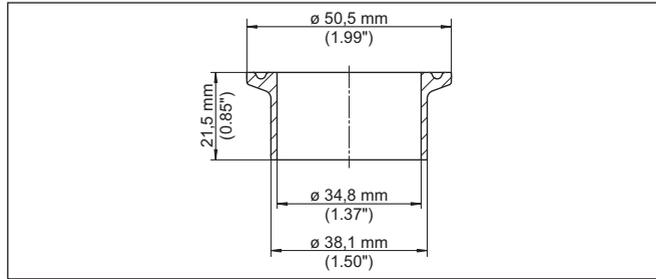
Medidas racor para soldar Clamp 1½" (DIN 32676, ISO 2852) PN 16
